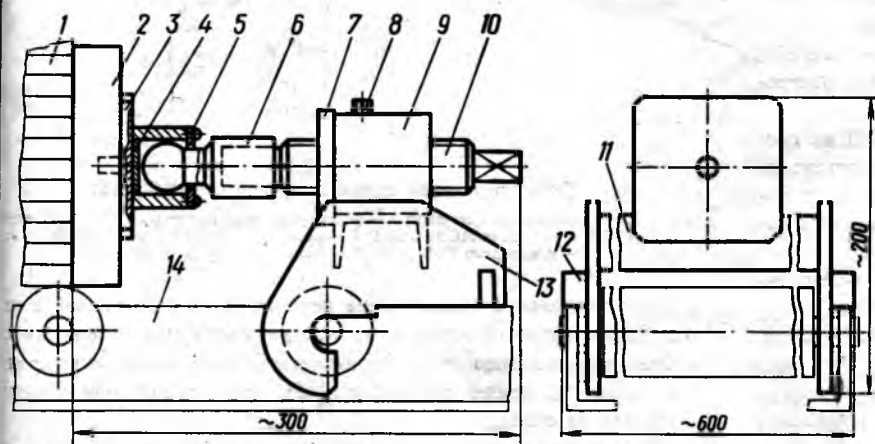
Схема приспособления для фиксации пакетов щитов ДСП:
